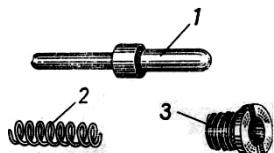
Деталі інертного (поворотного) бойка: 1 – бойок із вінцем; 2 – поворотна пружина; 3 – муфта з різьбленим для кріплення в корпусі колодки (брандтрубка).
